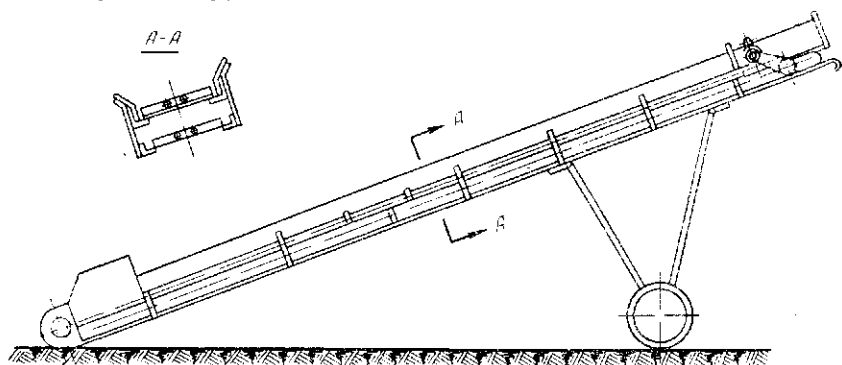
Цепочно-скребковый транспортер СТ-2.
